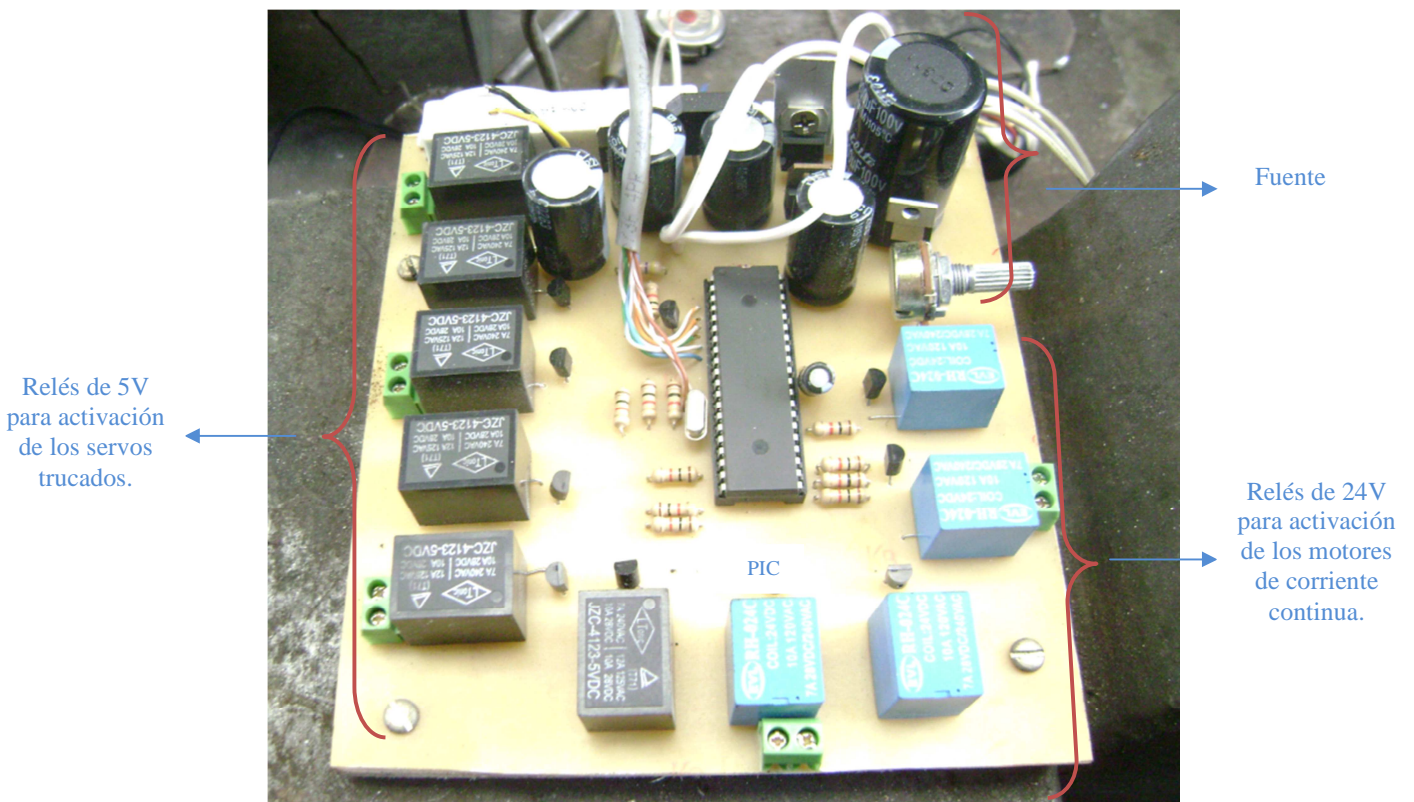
Circuito de control del Brazo robótico completamente soldado.
